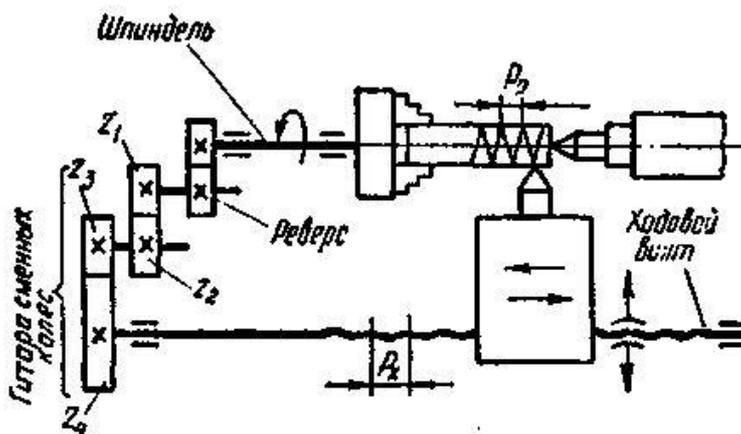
Схема цепи движения подачи при нарезании резьбы
